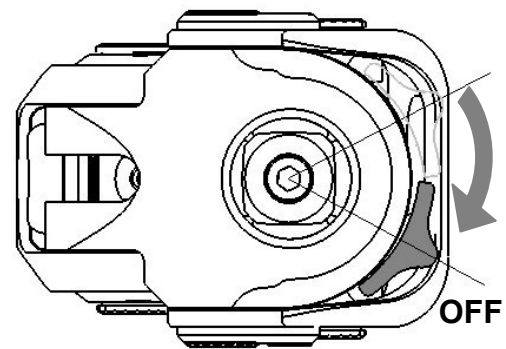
Posizione di sbloccaggio della leva (vista dall'alto)
